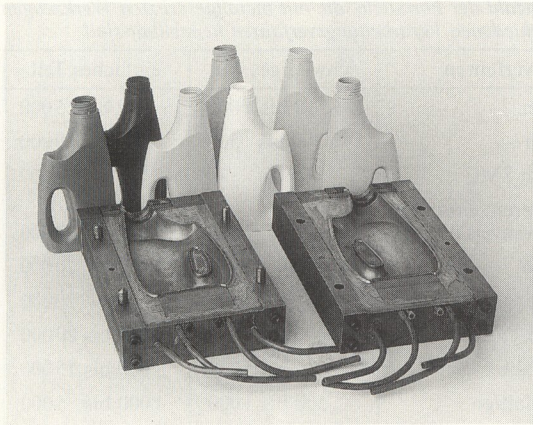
Metallgespritztes Blasformwerkzeug für Flaschen
